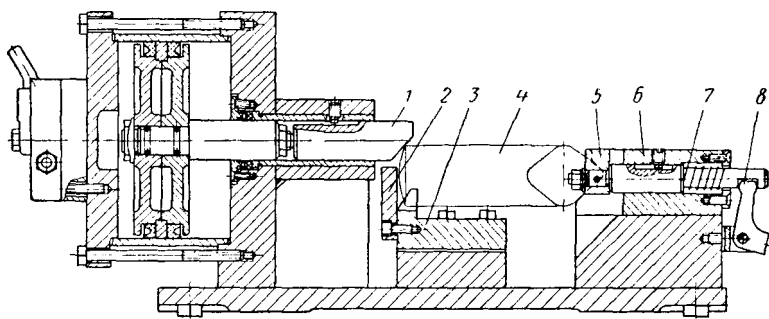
Приспособление для фрезерования наружных плоскостей вилок
